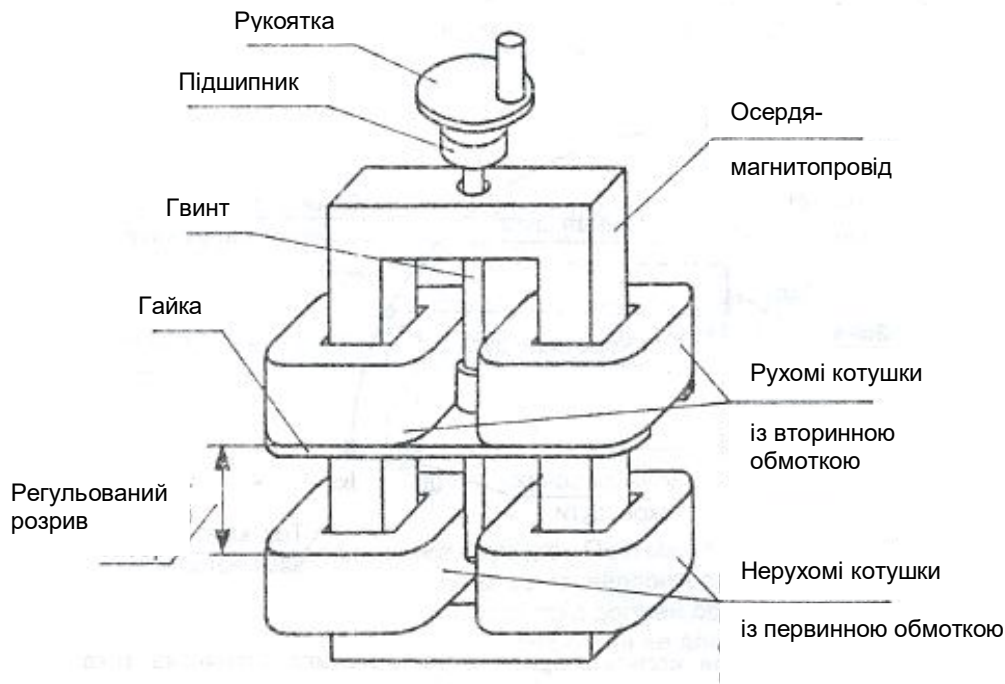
Конструктивна схема зварювального трансформатора з рухомими котушками вторинної обмотки
